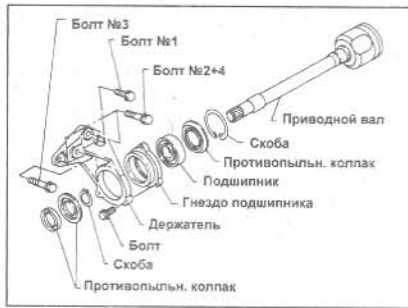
Сборка подшипника держателя - только модели 1.8 и 2.0 литра (Глава 4)
